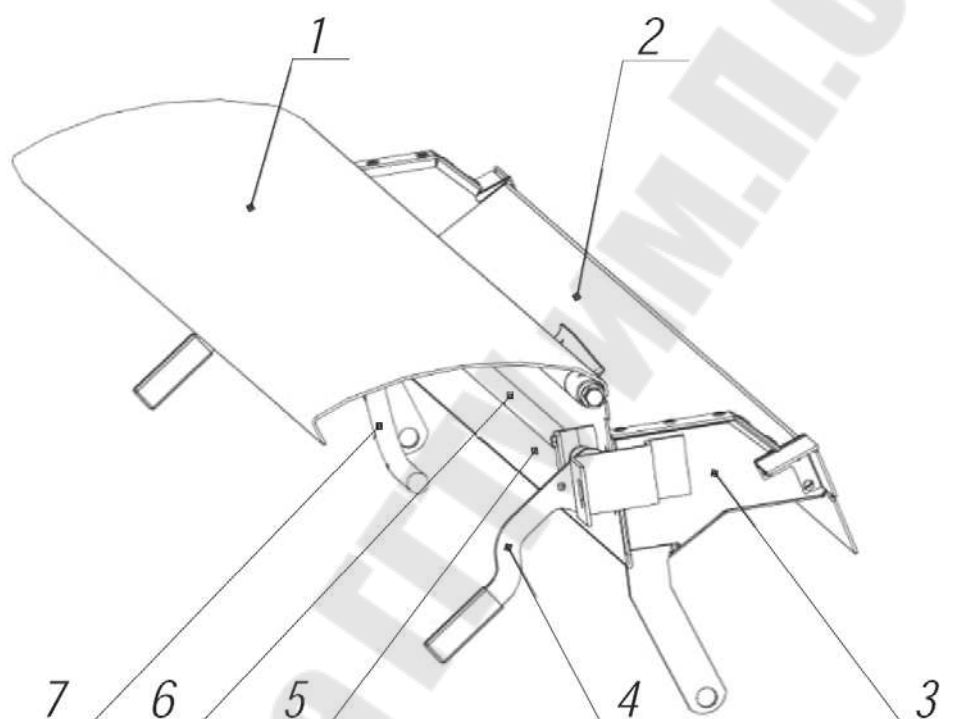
Конструктивная схема камнеуловителя: 1 – щит; 2 – основание; 3 – боковина; 4 – рукоятка; 5 – крышка; 6 – ось; 7 – ручка
